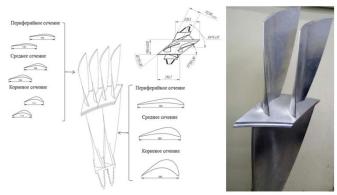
Трехмерная модель и опытный образец «вильчатой» рабочей лопатки паровой турбины
